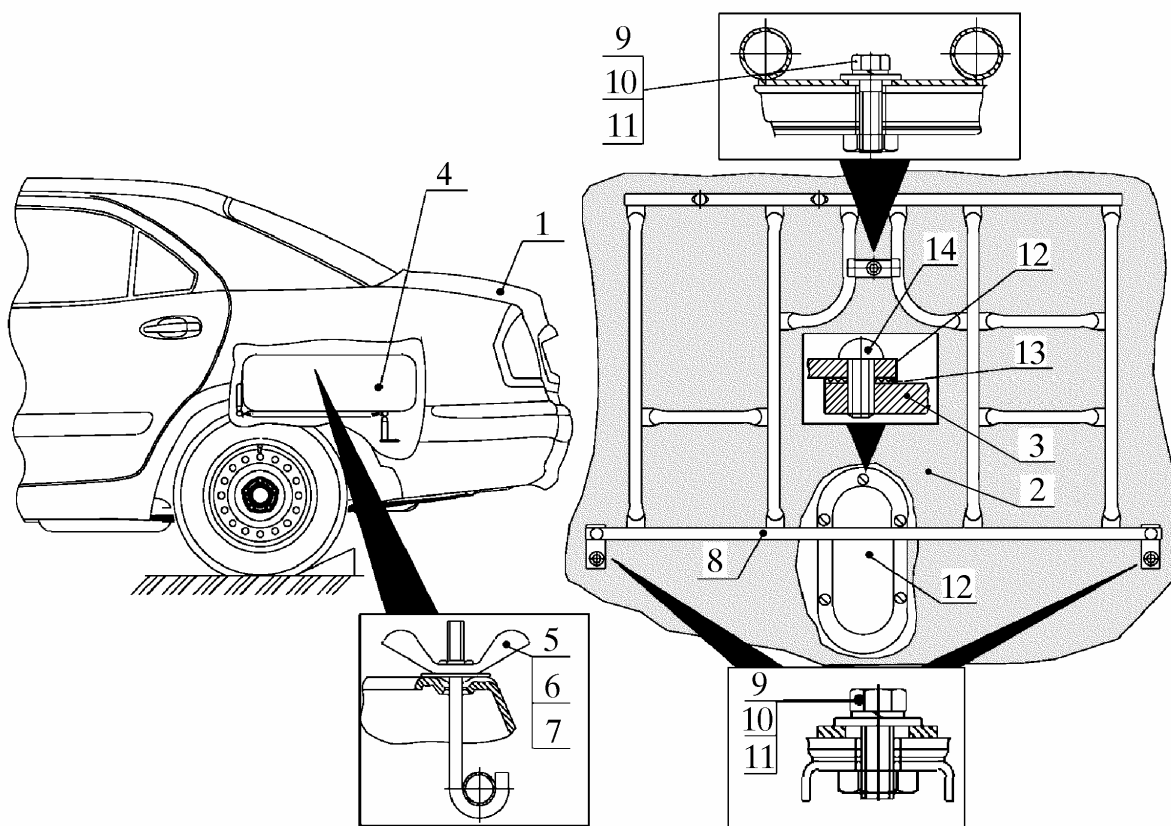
Снятие запасного колеса, его держателя и крышки люка:
